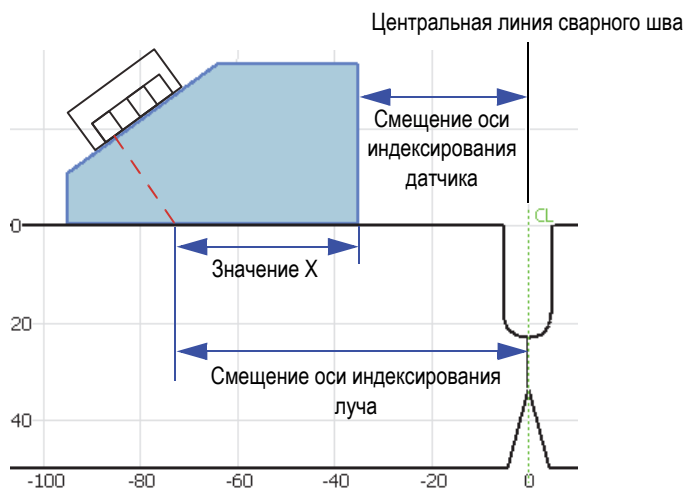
Смещение оси индексирования луча при контроле сварного шва
